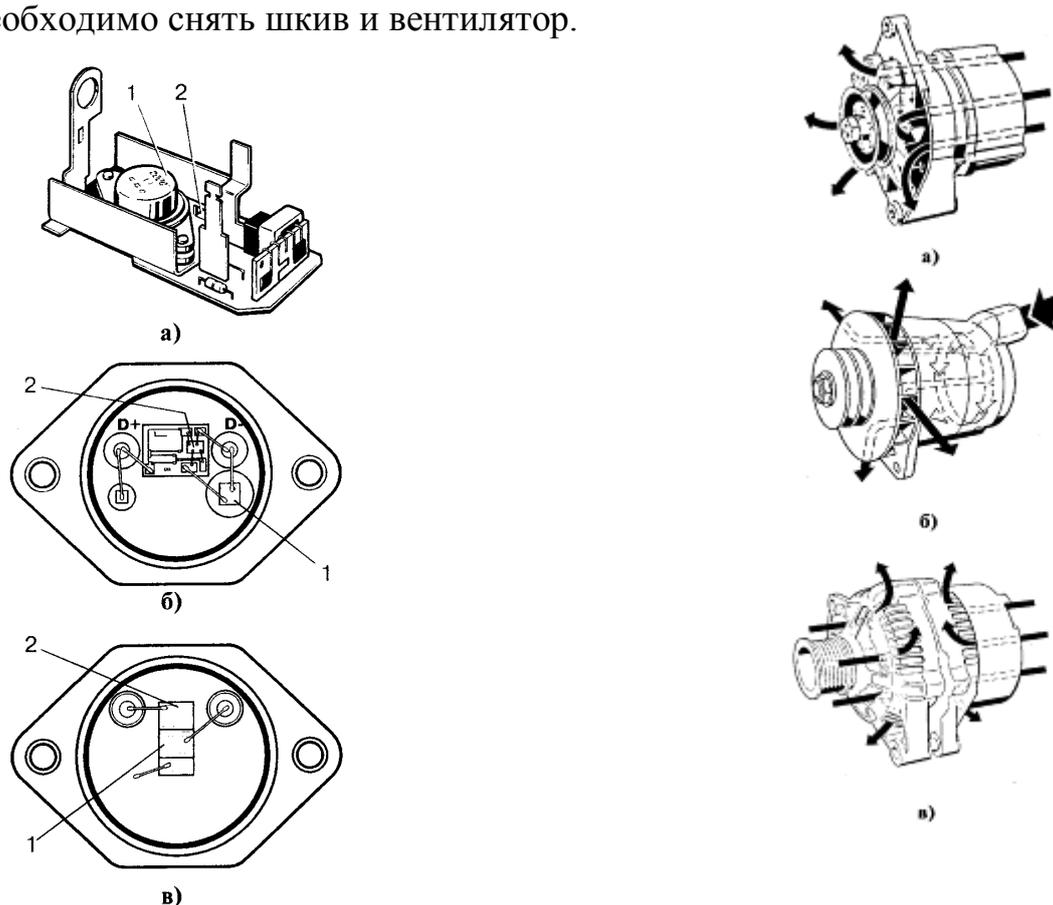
Регуляторы напряжения фирмы Bosch различного исполнения. а - на дискретных элементах; б - гибридный монтаж; в - схема на монокристалле кремния. 1 - силовой выходной каскад, 2 - схема управления
